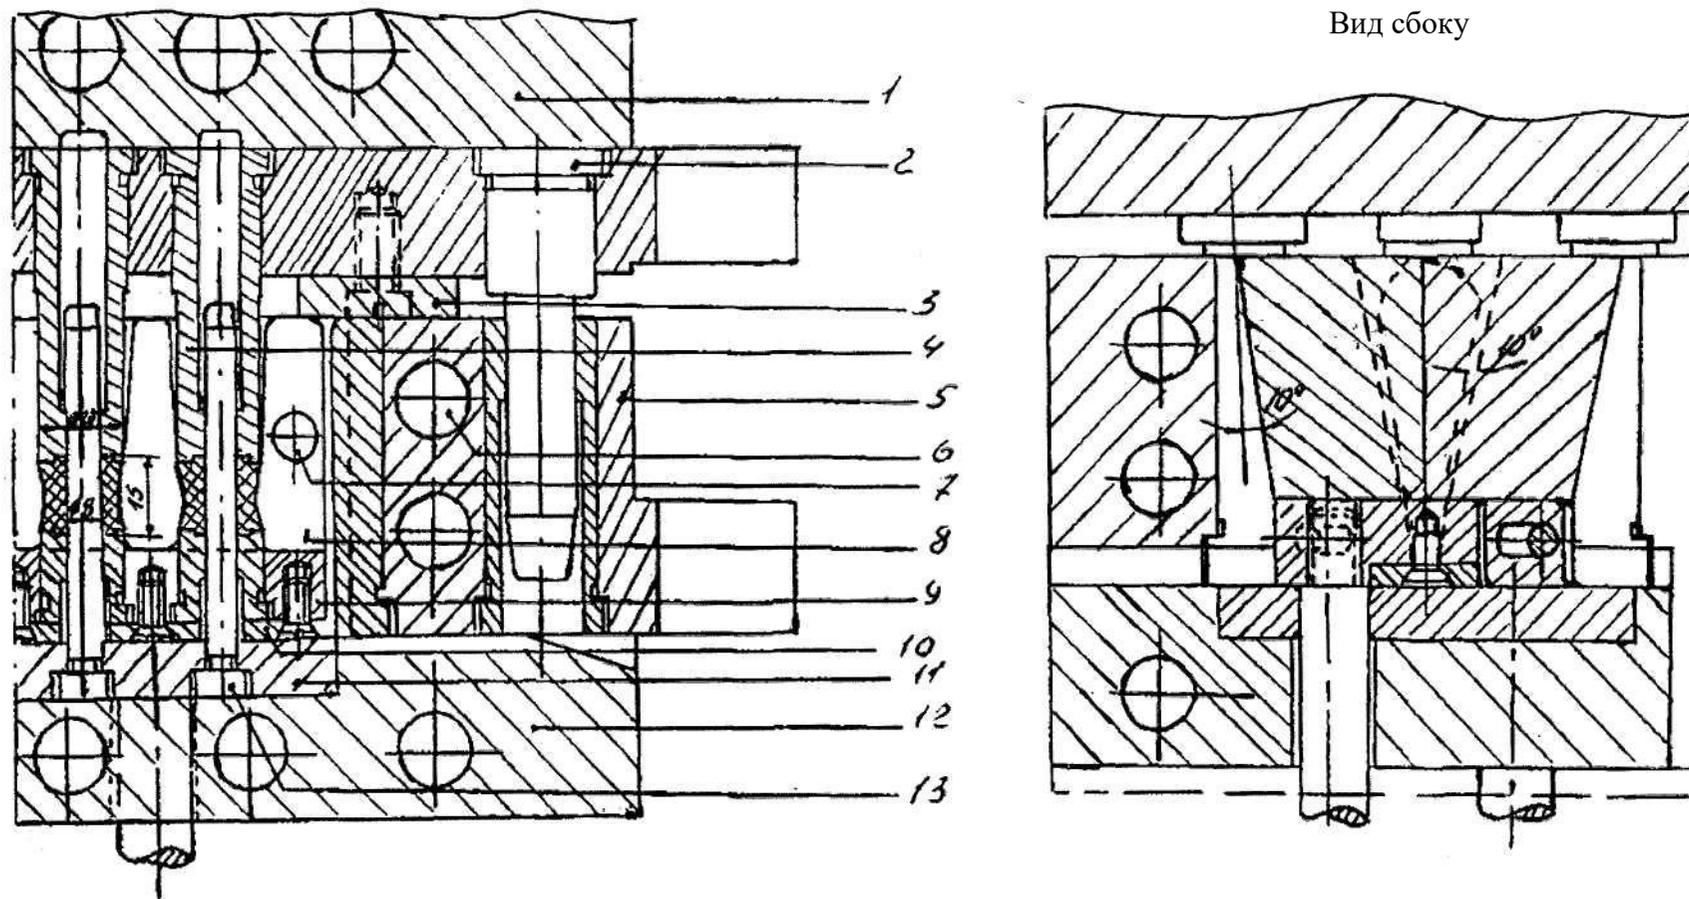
Пресс-форма для изготовления деталей методом прессования:
